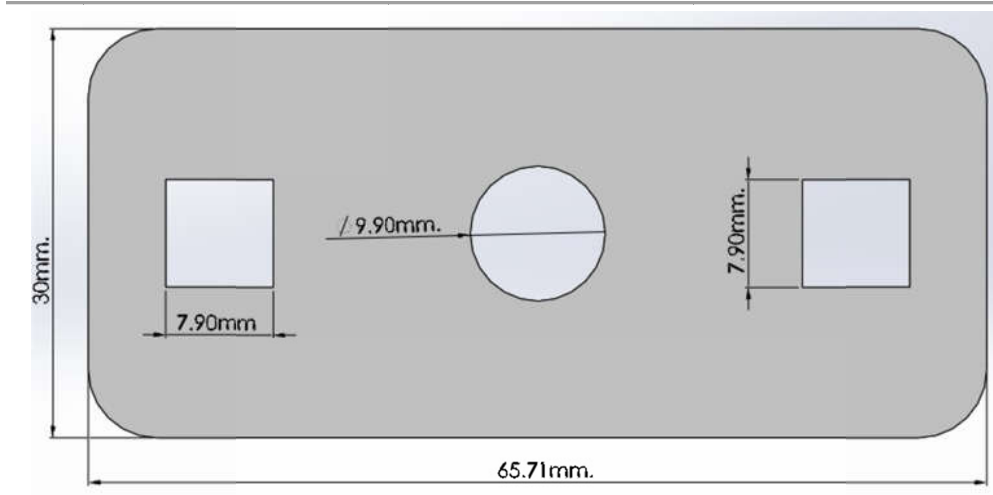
Pieza 4 del soporte para introducir las bobinas y la punta de prueba al magnetómetro.
